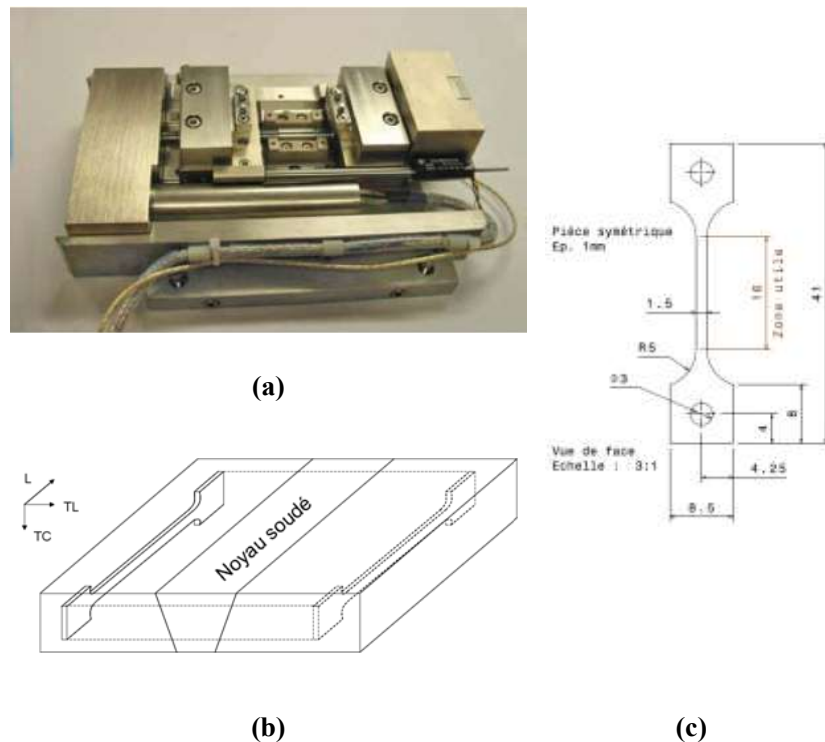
(a) Platine de microtraction DEBEN équipée d'une cellule de force de 5 kN (b) Schématisation du prélèvement des éprouvettes de microtraction dans les joints soudés (c) Dimensions des éprouvettes de microtraction.
